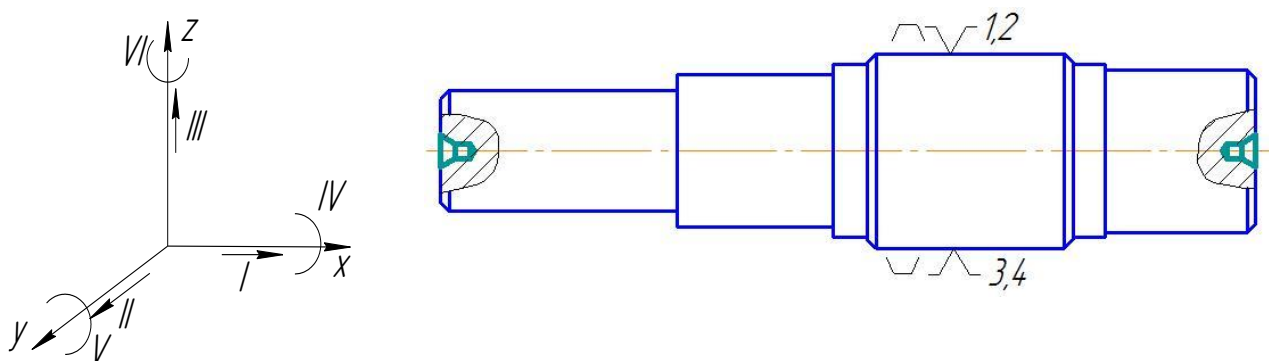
Ескіз обробки заготовки на операції 005
